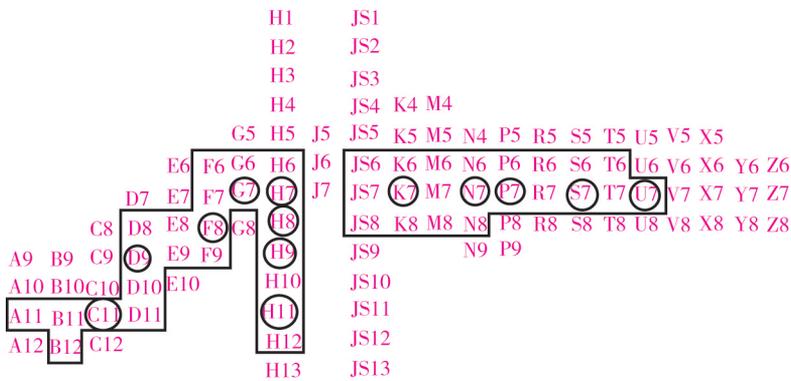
孔的一般、常用和优先公差带（尺寸 ≤ 500 mm）
